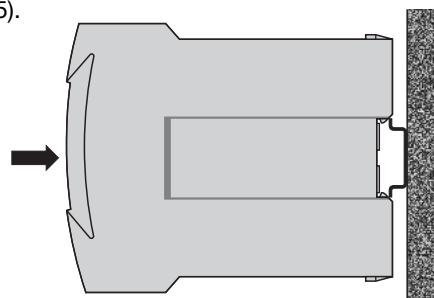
Montage sur rail «à chapeau» 35 × 15 ou 35 × 7,5 mm.
